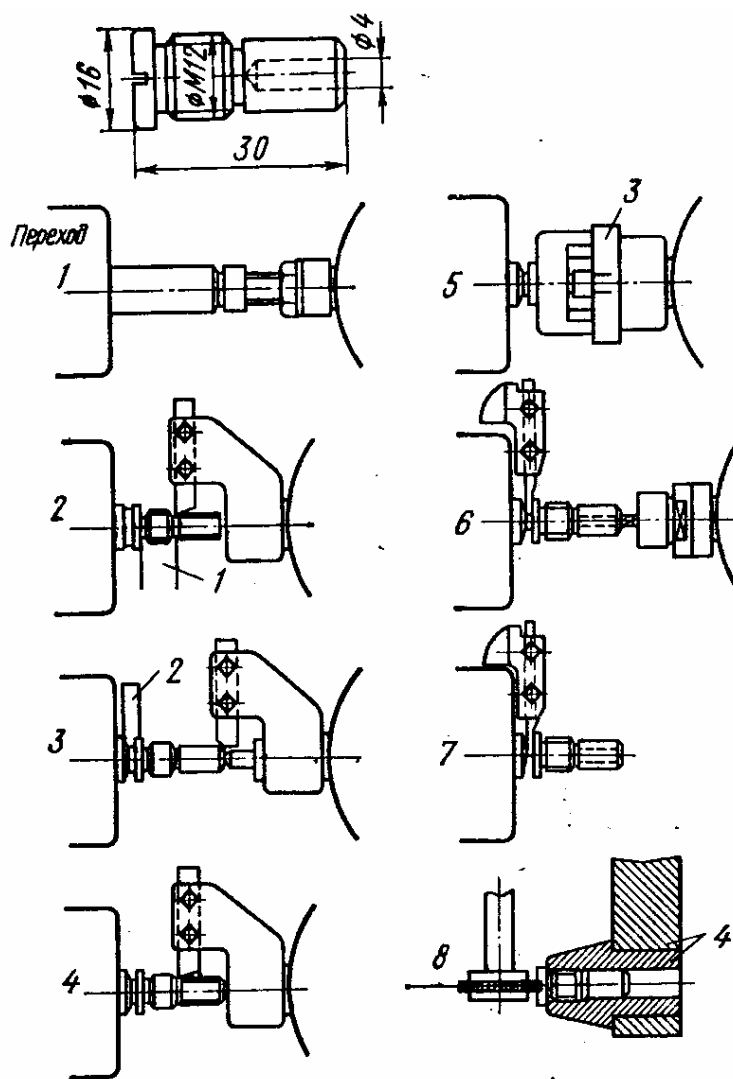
Схема наладки токарно-револьверного автомата для обработки винта диаметром М12. Наименования переходов: 1 – подача до упора, 2 – подрезка головки и обтачивание ступени стержня под резьбу фасонным резцом 1, 3 – протачивание закругления головки резцом 2 с поперечного суппорта и снятие фаски и зацентровка с револьверной головки, 4 – чистовое обтачивание стержня с револьверной головки, 5 – нарезание резьбы посредством резьбонарезного патрона 3, 6 – начало отрезки детали с поперечного суппорта и сверление отверстия с револьверной головки, 7 – окончание отрезки детали, 8 – фрезерование шлица в специальном приспособлении-захвате 4
